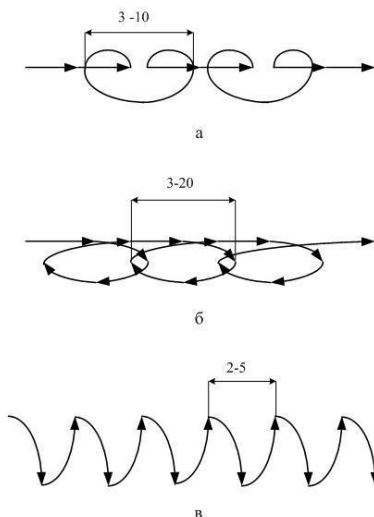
Схемы перемещения электрода при сварке плавящимся электродом в защитных газах для увеличения ширины шва: а и в – для получения равномерного провара по всей ширине шва, б – для получения плавного перехода от усиления шва к основному металлу на одну сторону от его продольной оси.
